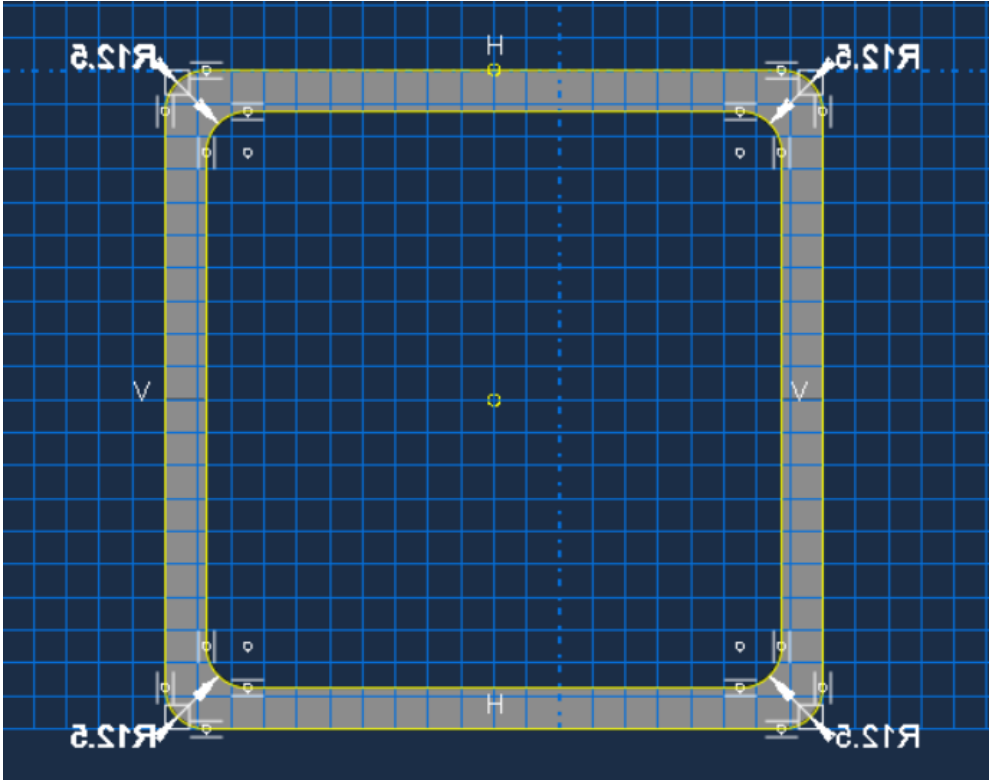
Croquis acotado del perfil del tubo cuadrado estructural
